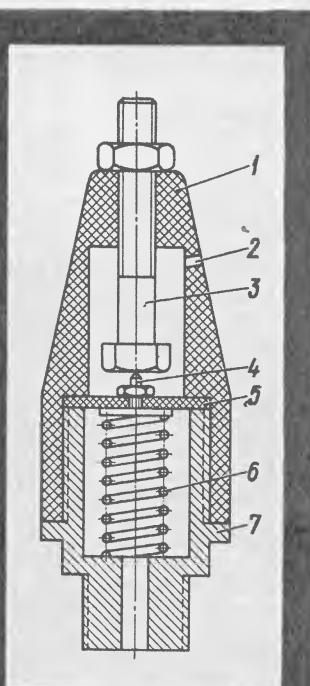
Самодельный вакуумный датчик включения сигнальной лампы: 1 — крышка из пластмассы; 2 — отверстие в крышке для прохода воздуха; 3 — регулировочный болт; 4 — контакт; 5 — диафрагма; 6 — спиральная пружина; 7 — металлический корпус
